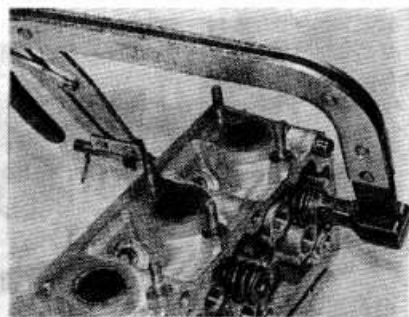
Приспособление для сжатия клапанных пружин (выпускной клапан N 1) — двигатель 2,0 л с одним распредвалом
